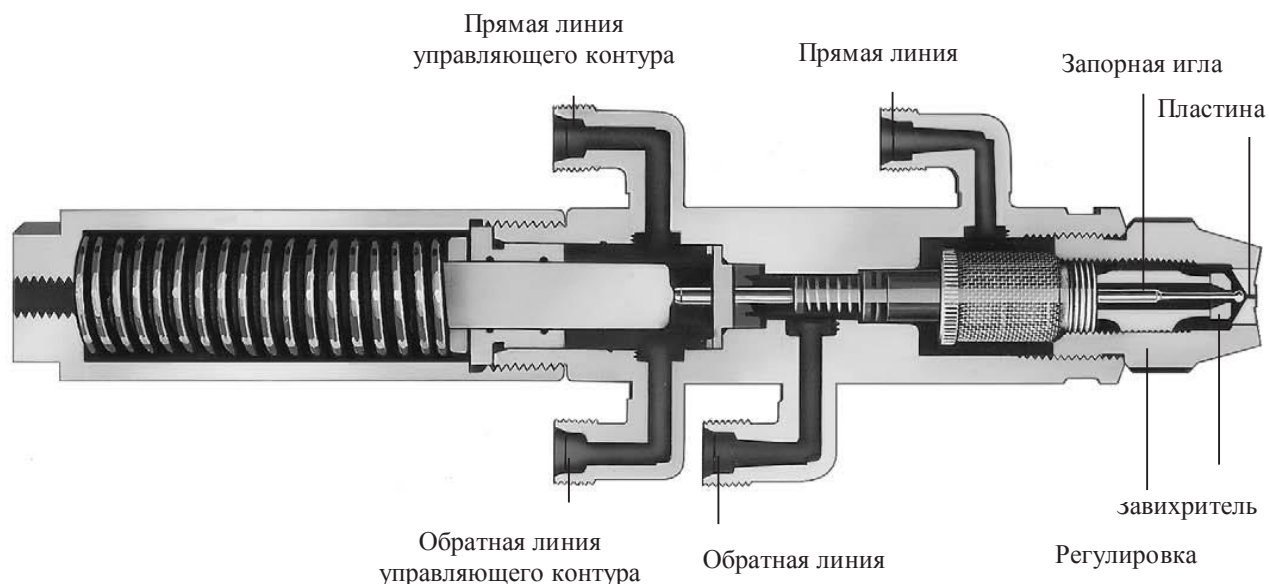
Форсуночный блок плавно-двухступенчатой и модулируемой горелки
